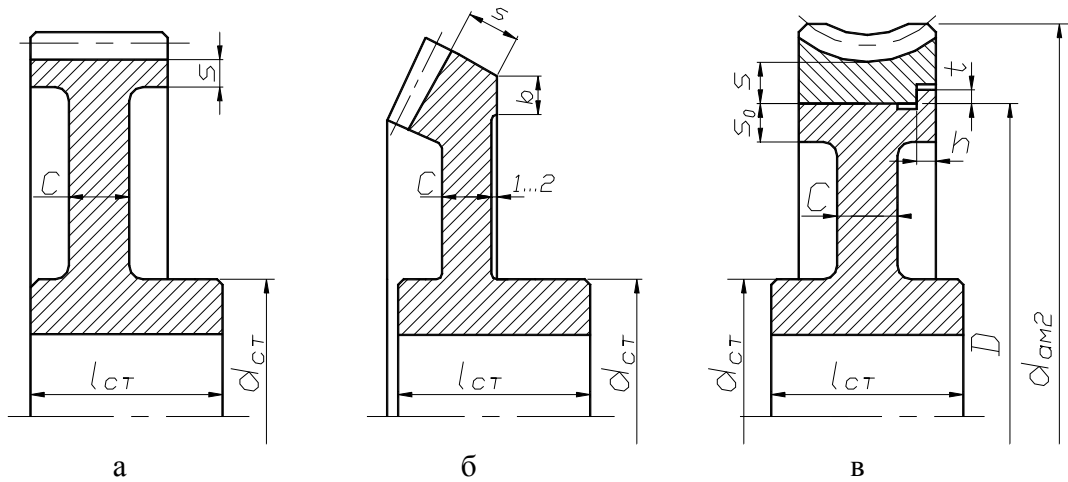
5. Эскизы колес: а – цилиндрическое колесо;
